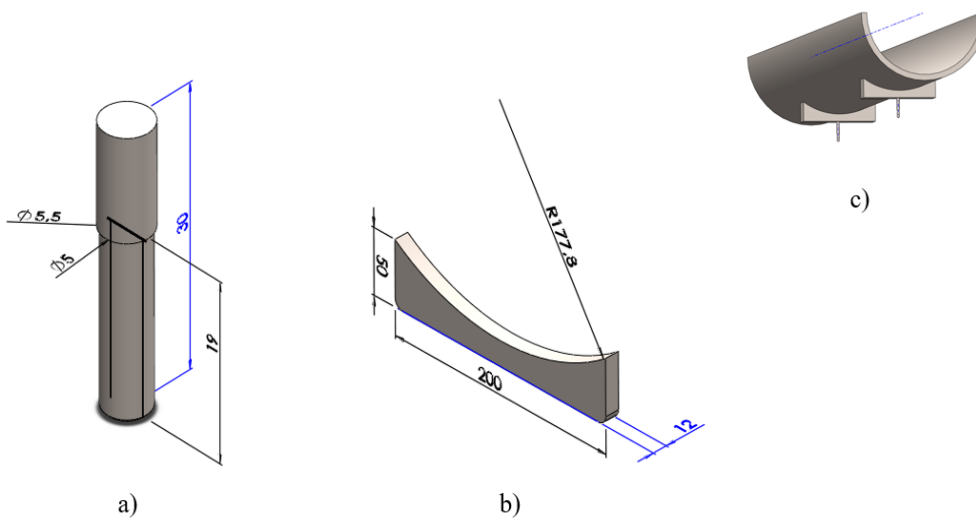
a) Dimensões do veio semi-roscado (mm); b) Dimensões do suporte (mm); c) Vista em perspectiva do subconjunto.
